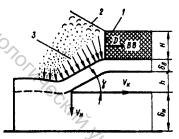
Схема установившегося процесса сварки взрывом:
